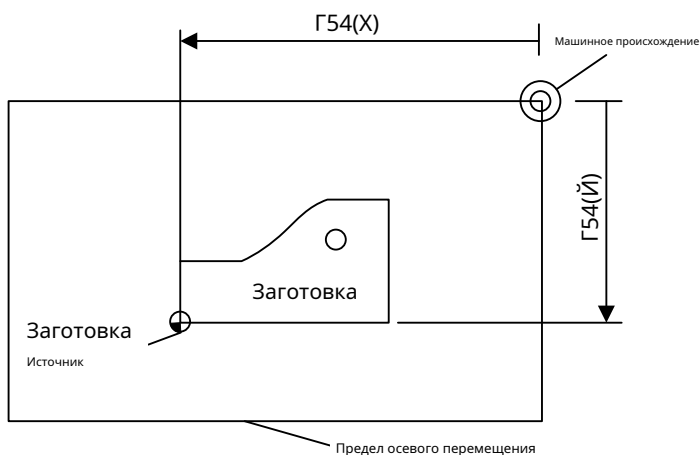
Связь между смещением заготовки и системой координат станка
